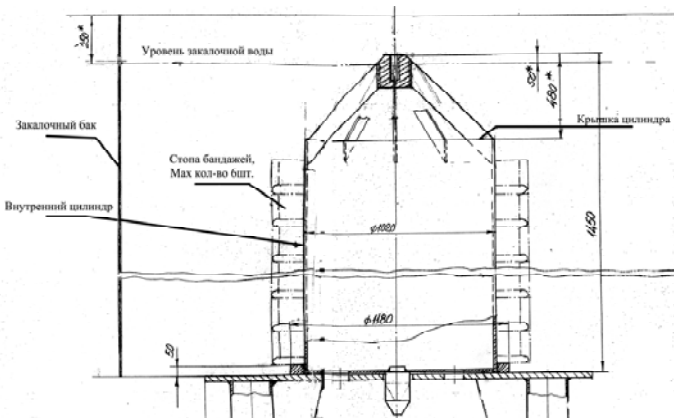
Принципиальная схема закалочного бака с приспособлением термозащиты внутренней поверхности стопы.
